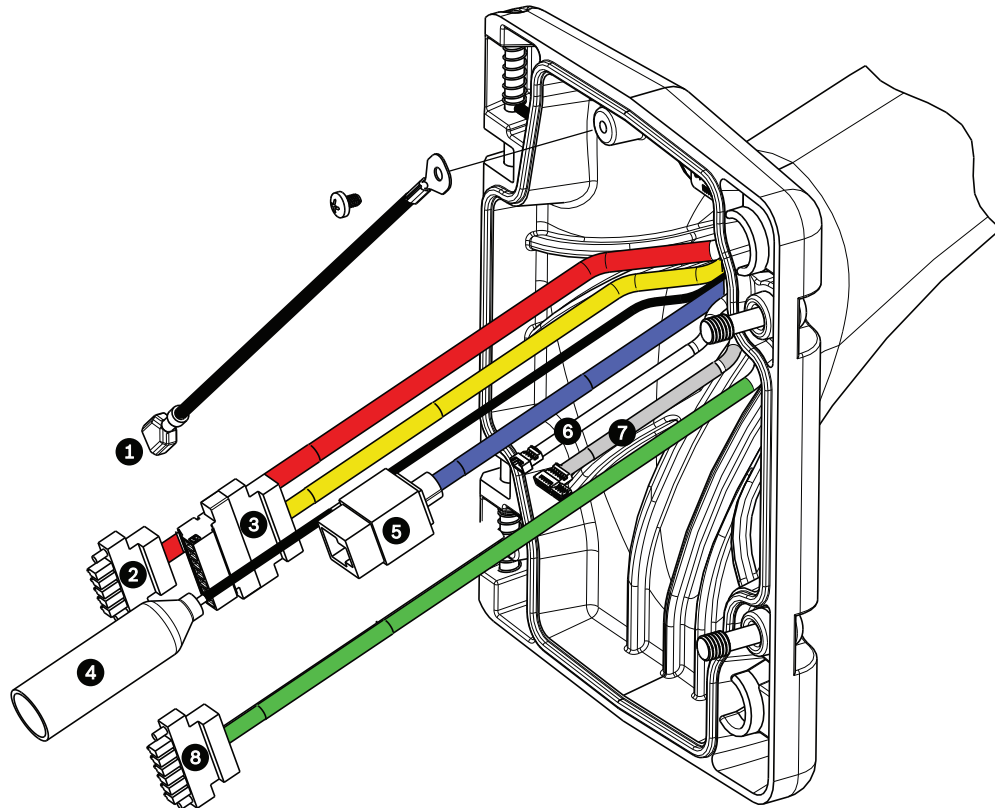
Подсоединение подвесного кронштейна к монтажной плате
